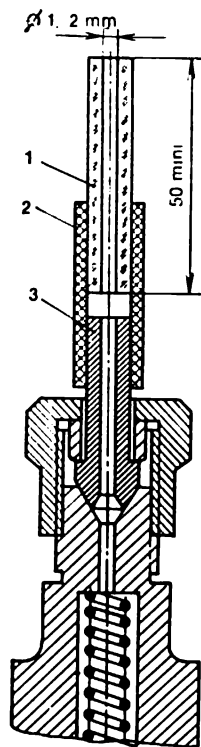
Montage du tube viseur du début d'injection: 1 — tube en verre; 2 — tube en caoutchouc; 3 — conduite haute pression
